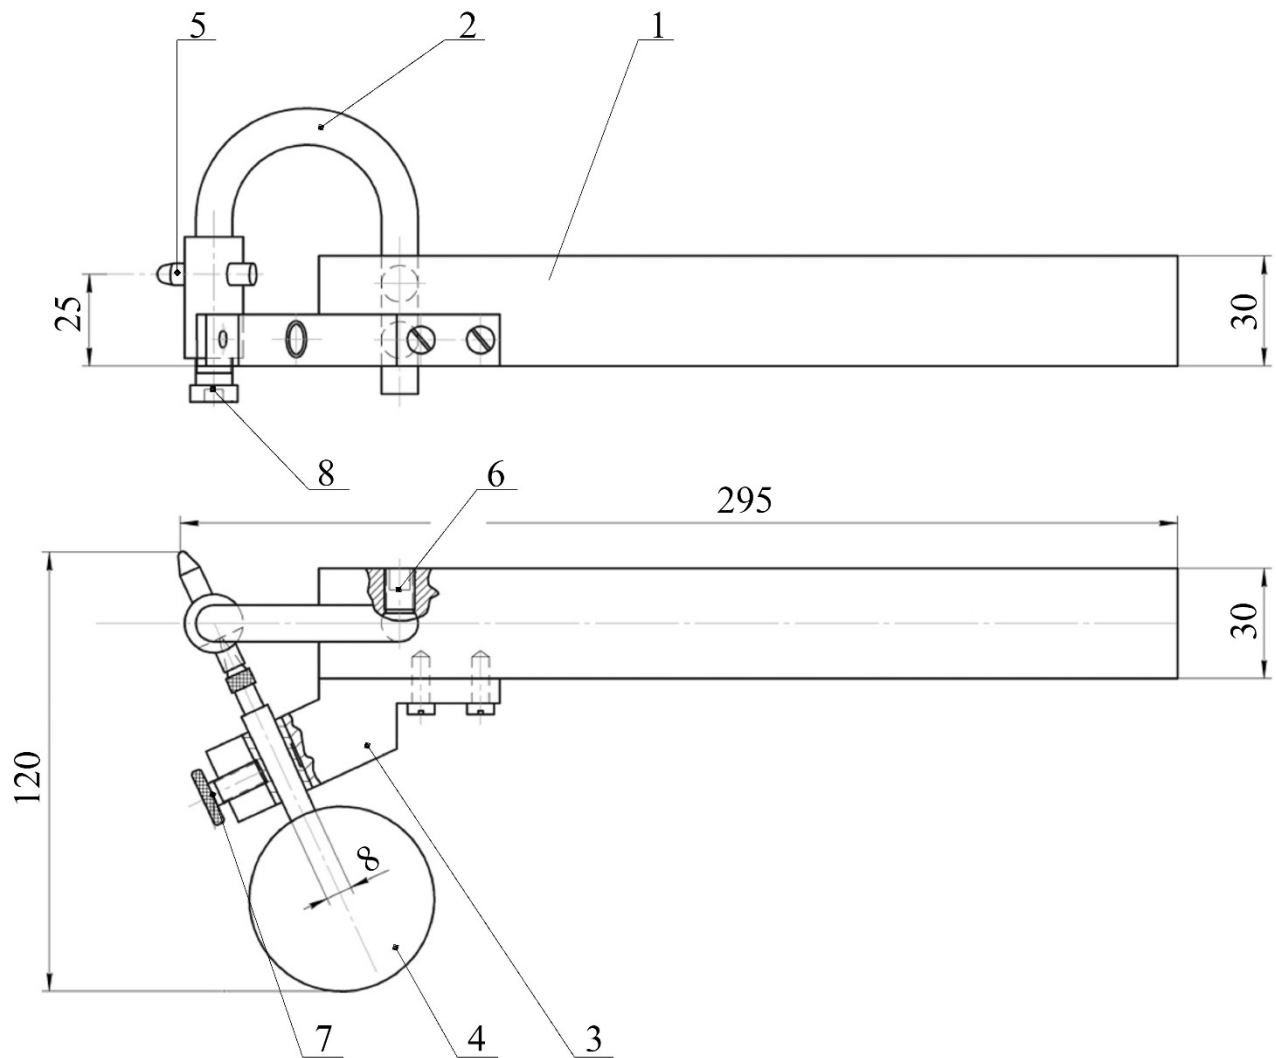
Конструкція оправки для алмазного вигладжування конструктивного концентратора напружень типу «Поверхня поєднання двох діаметрів»
